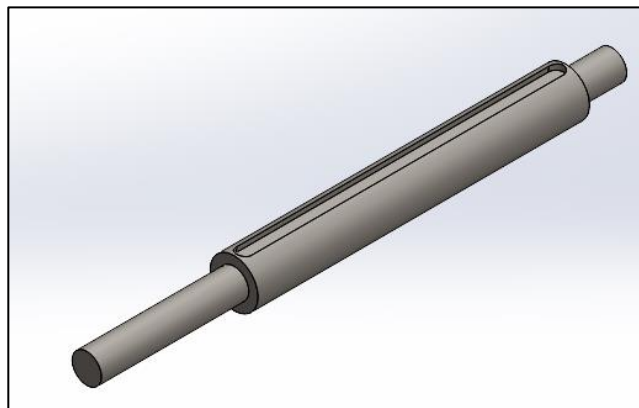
Vista isométrica del eje de la máquina trituradora en SolidWorks
